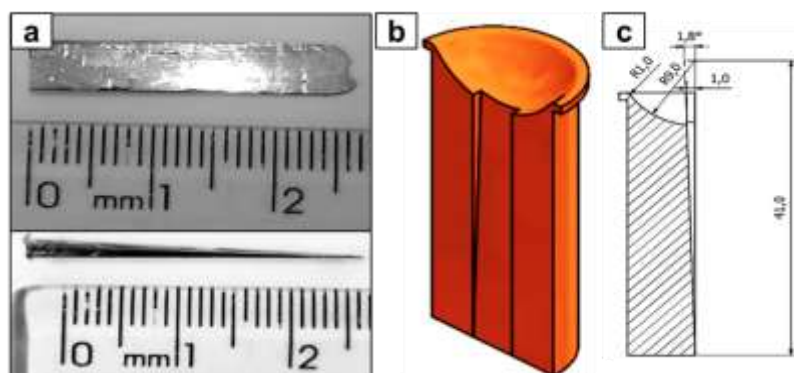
a) Cunha fundidas em molde de cobre com sistema de sucção, b) desenho do molde de Cu e c) vista esquemática de perfil com as medidas do molde.
